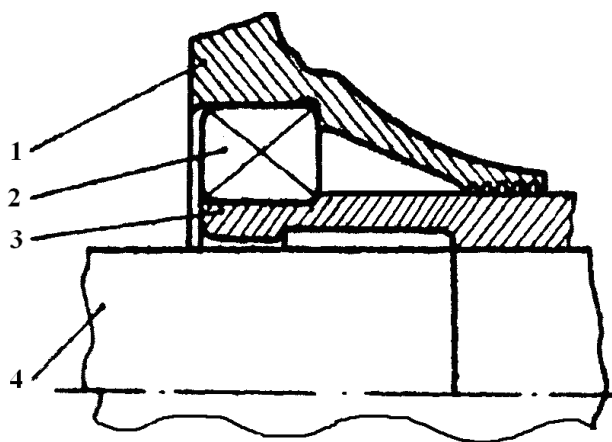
Підшипниковий вузол гідравлічного насоса: 1-корпус робочого колеса насоса; 2 – підшипникова опора; 3 – консольний - пружний елемент; 4 – вал робочого колеса
